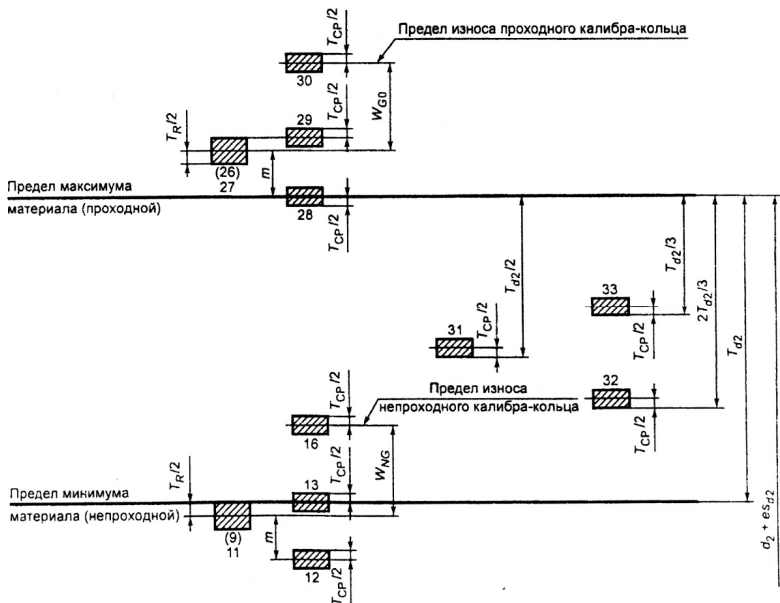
Схемы расположения полей допусков среднего диаметра калибров для контроля наружной резьбы по ГОСТ 4608 с сортировкой на группы
